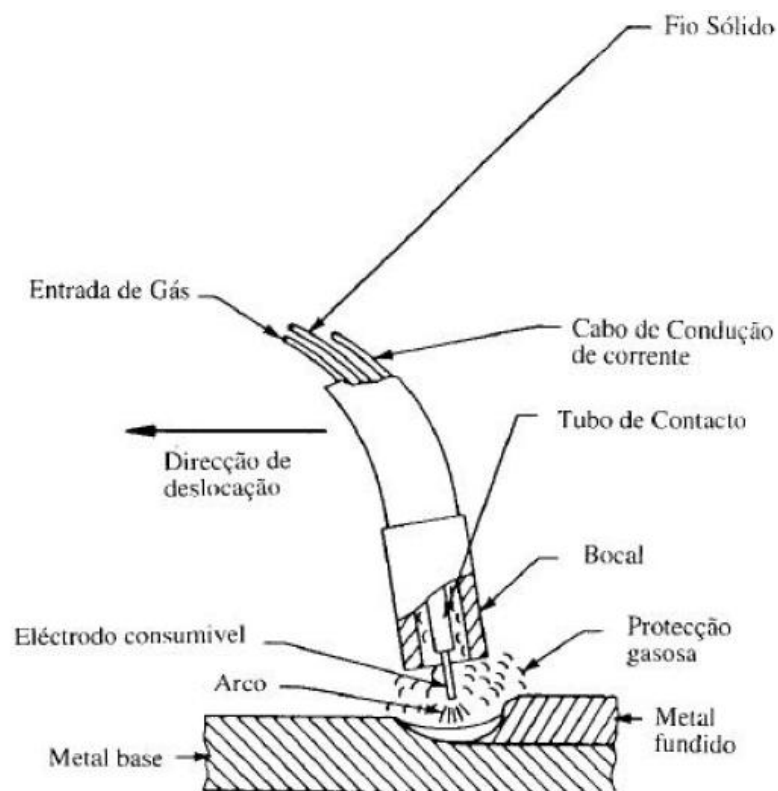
Forma de actuar a soldadura MIG
